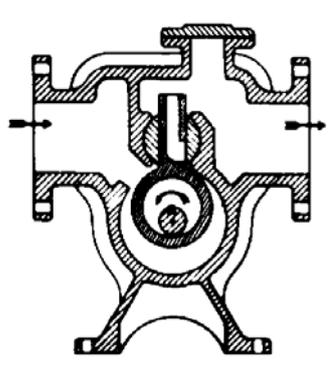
Corte de una Bomba Rotatoria de Pistón
